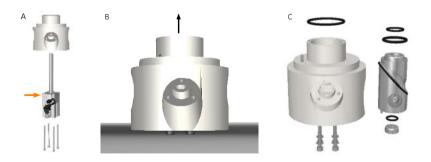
A: cilindro pneumatico e pistone, B: corpo esterno valvola di gestione fase mobile, premerla contro una superficie piana per espellere il corpo interno della valvola, C: o-ring sul corpo interno della valvola
